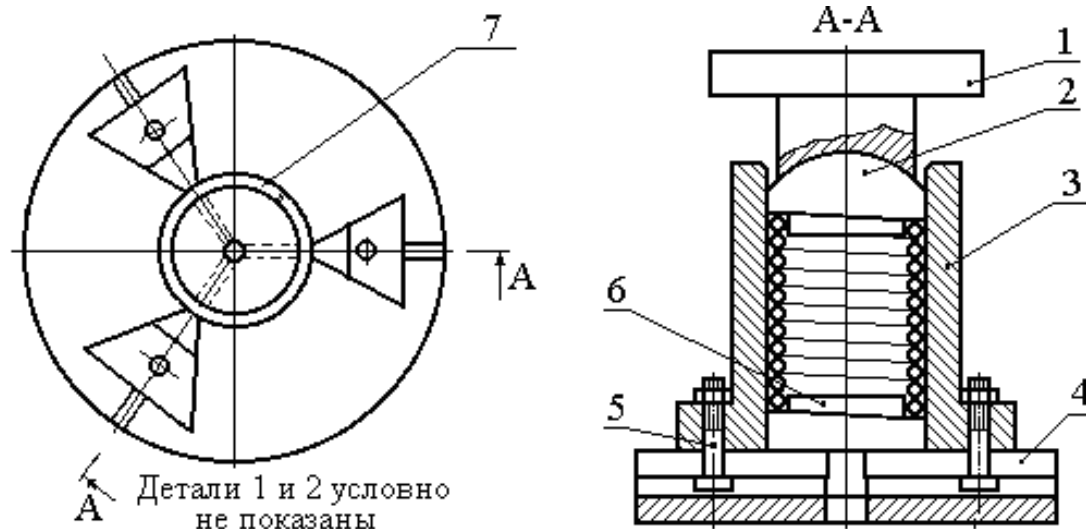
Устройство для заневоливания по пат. RU 2251037 [97]
